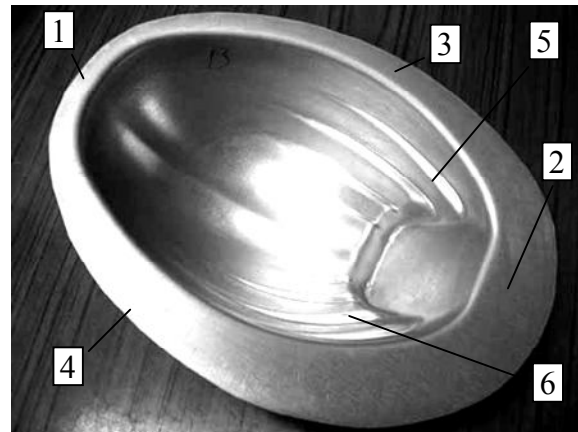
Образец № 13 со смещением исходной заготовки к задней призме:
